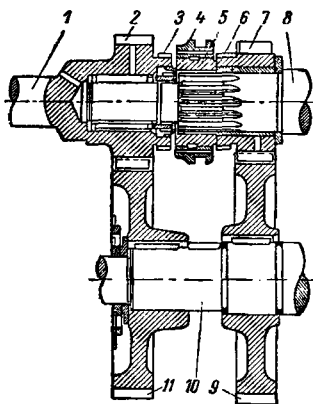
Схема коробки передач с шестернями постоянного зацепления и муфтой включения передач.
